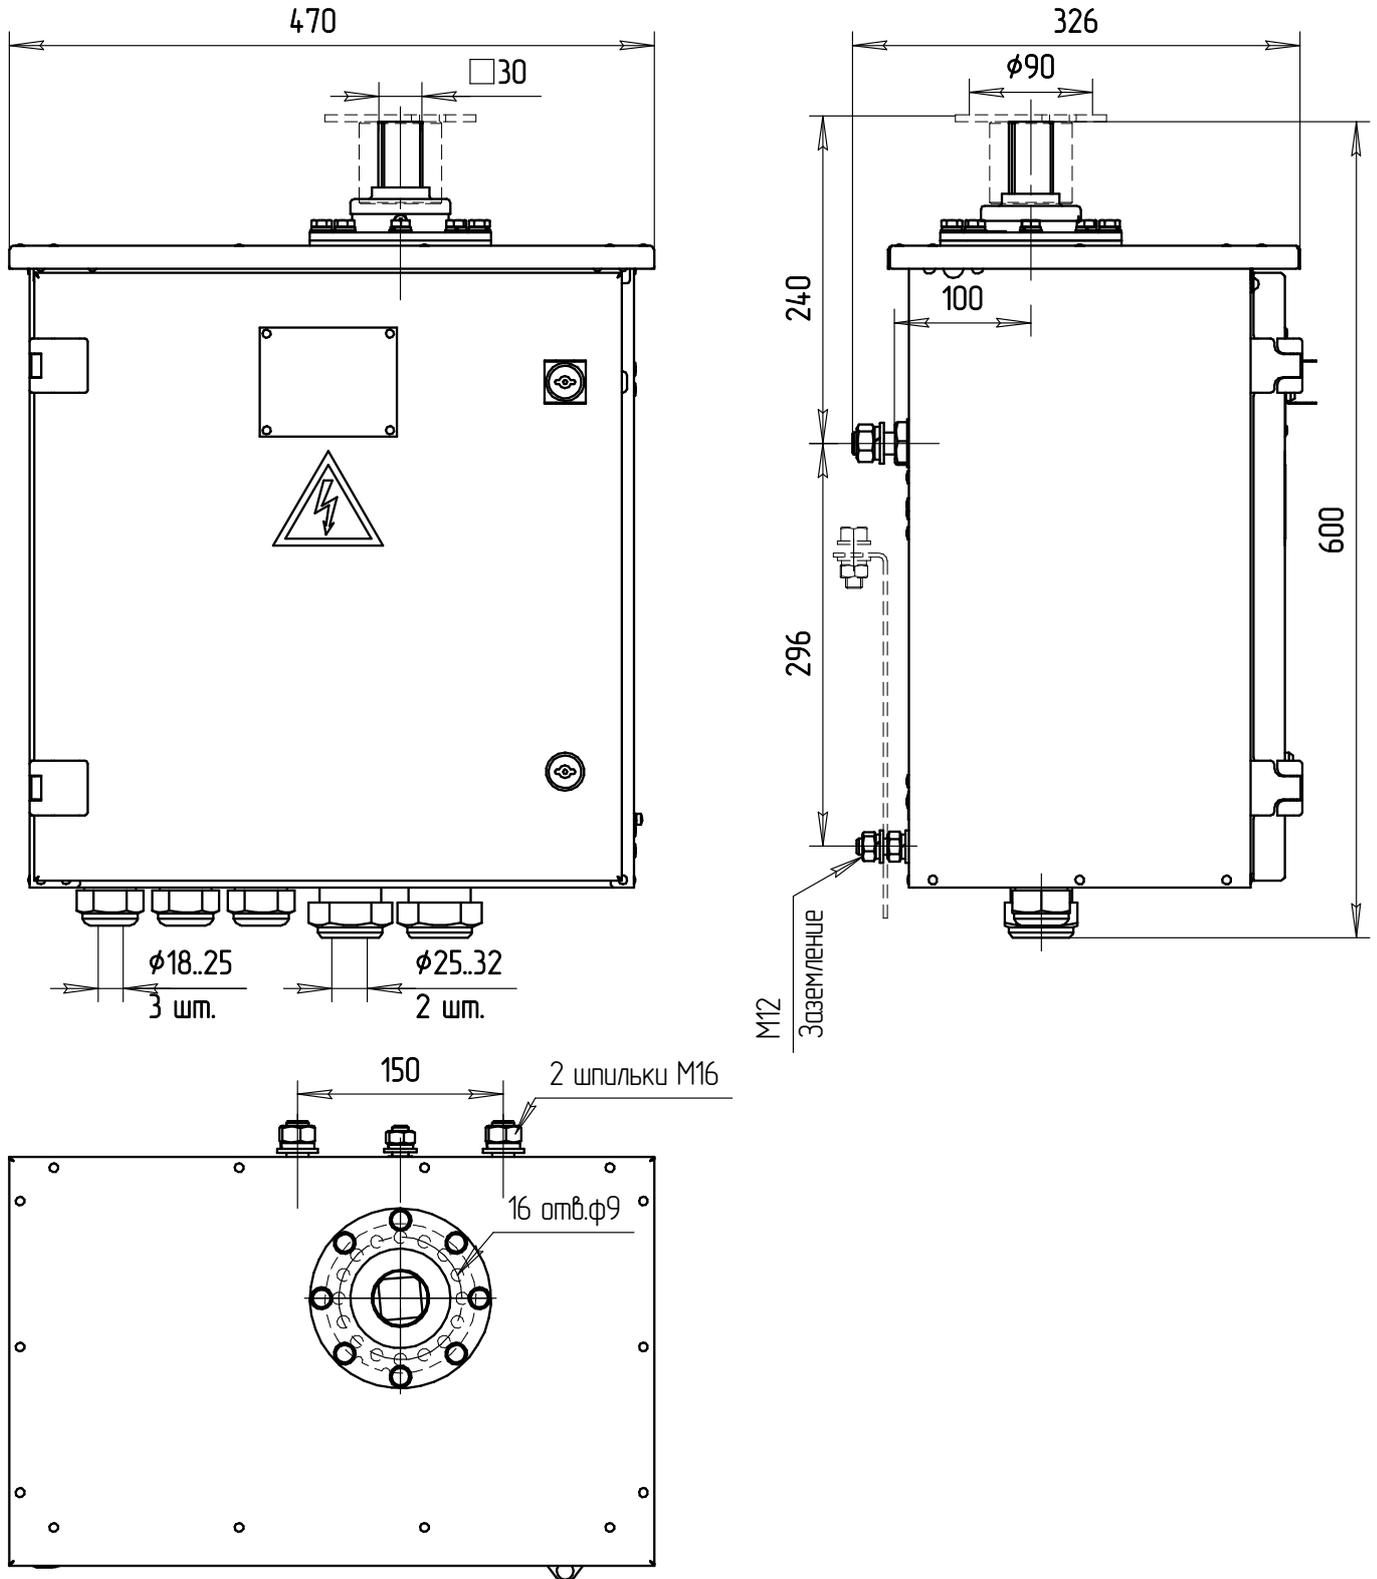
Общий вид привода ПД СЭЩ[®]-11-90 УХЛ1
